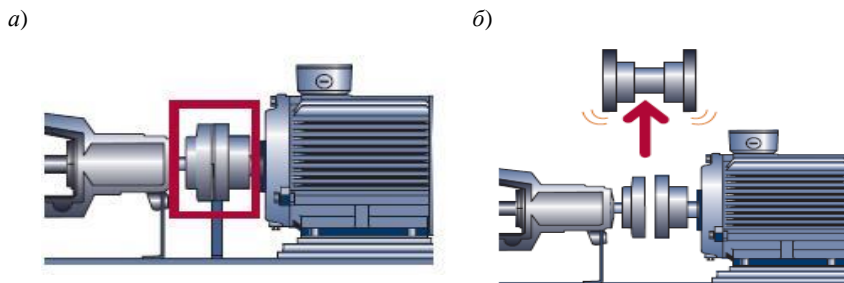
Центробежный насос с соединительной муфтой:
